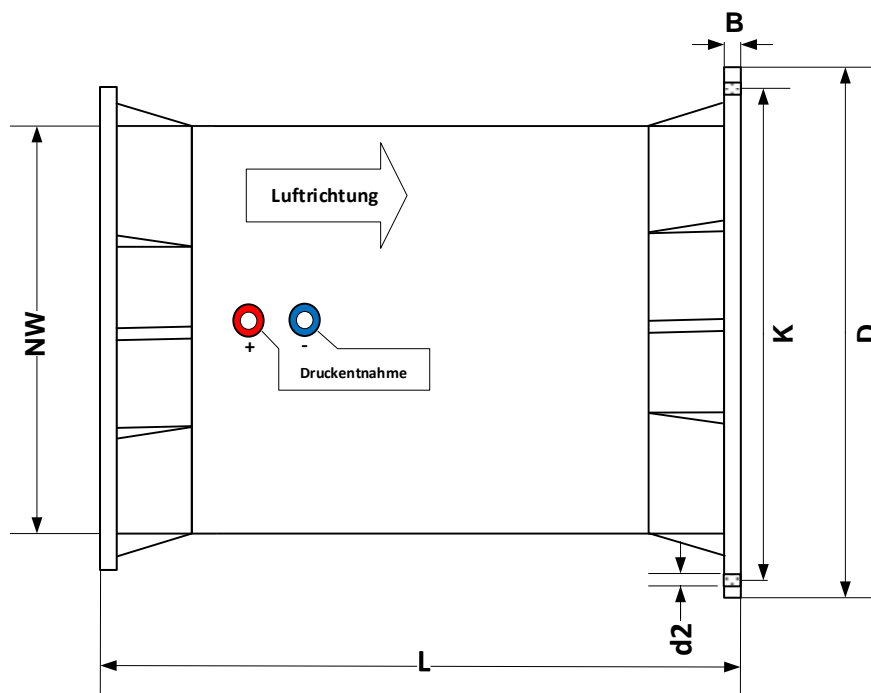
, Abmessungen Messeinrichtung rund Stahl Flansch/Flansch
